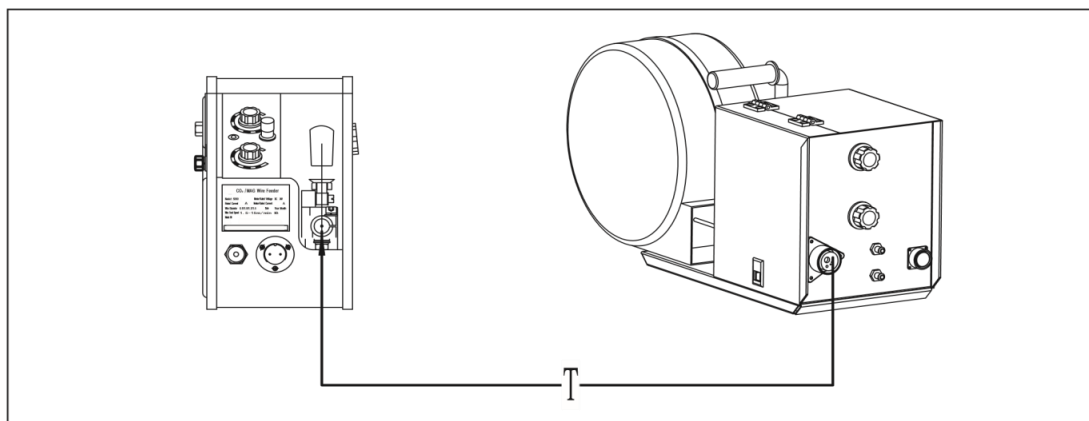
Подсоединение сварочной горелки
